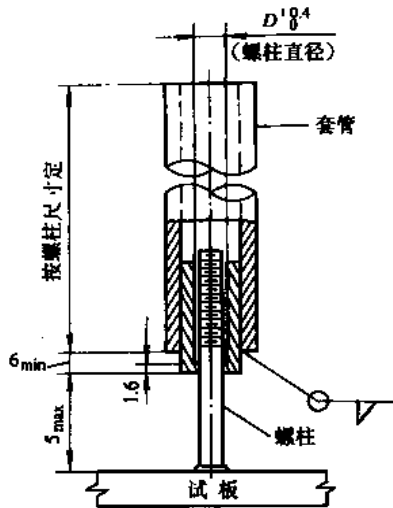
螺柱焊接头弯曲试验用夹头的形式和尺寸
